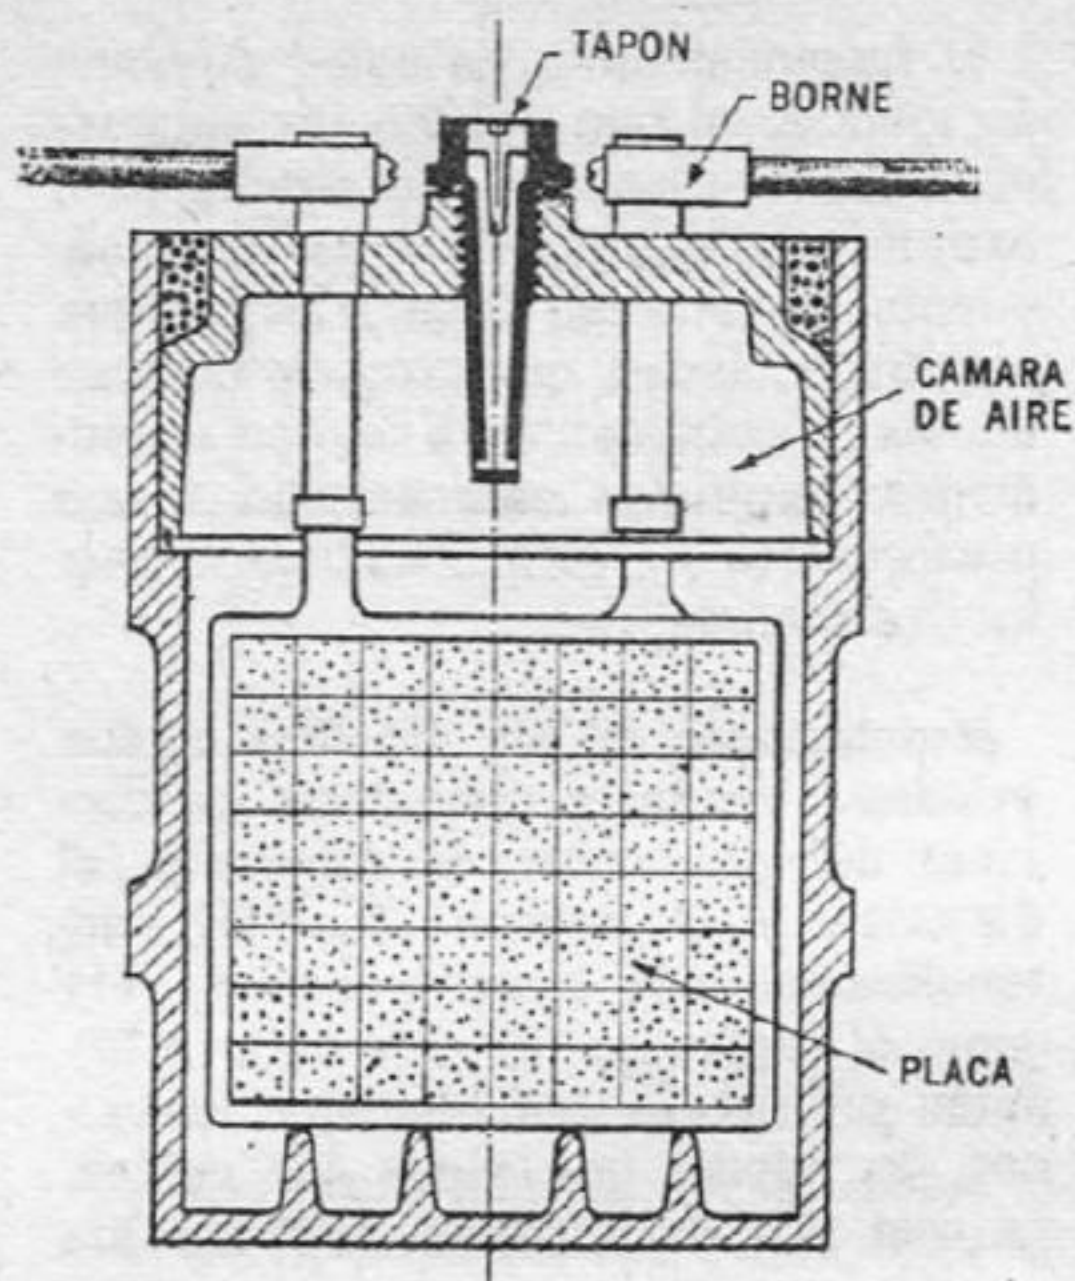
Corte de una batería para avión, con cámara de aire separadora.
